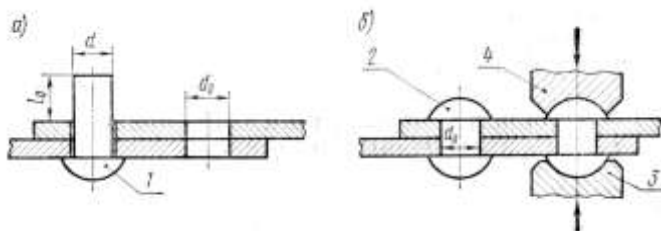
Образование заклепочного шва: *a* - закладка заклепки; *б* - клепка; 1 - закладная головка; 2 - замыкающая головка; 3 - поддержка; 4 - обжимка
